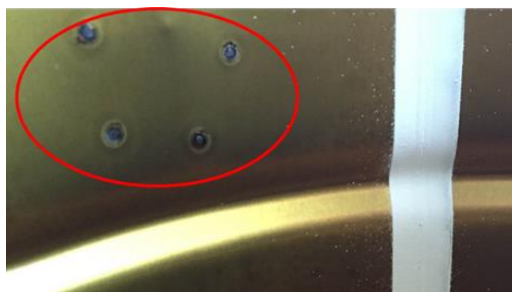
Orifícios resultantes da soldadura do olhal
